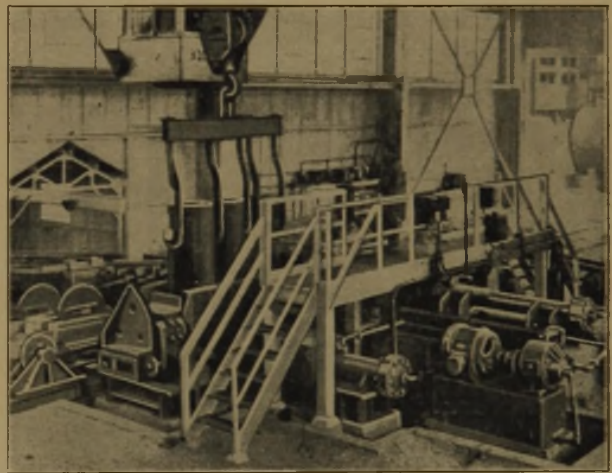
Rückansicht der Blockausdrückvorrichtung und Kokillengehänge.
